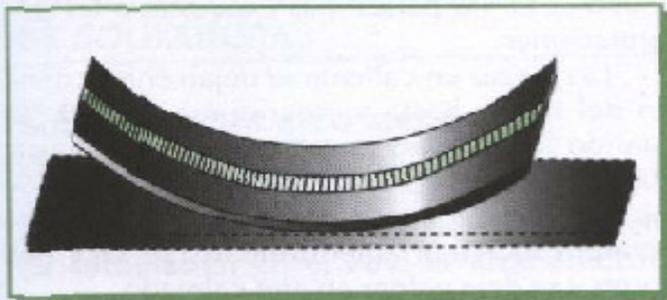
Deformación ocasionada por la soldadura en una pletina de pequeño espesor.
